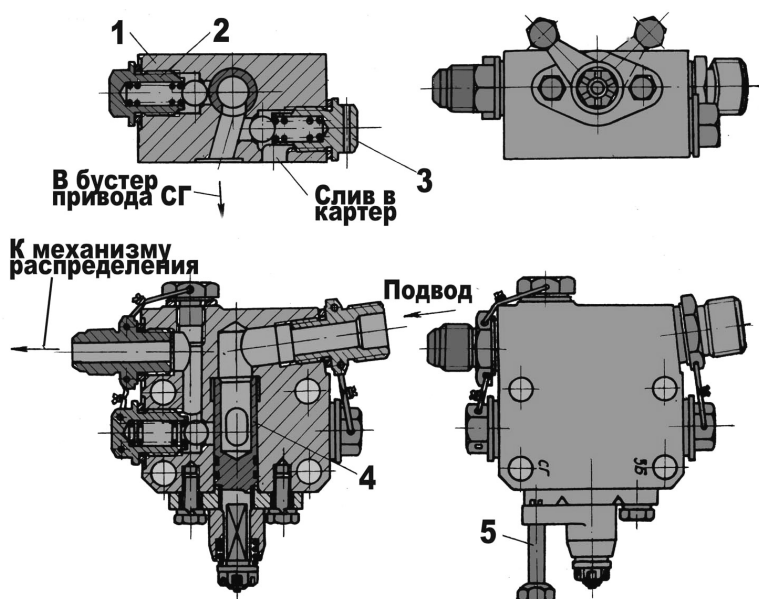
Кран-распределитель: 1 – корпус; 2 – обратный клапан; 3 – перепускной клапан; 4 – золотник; 5 – ручка
